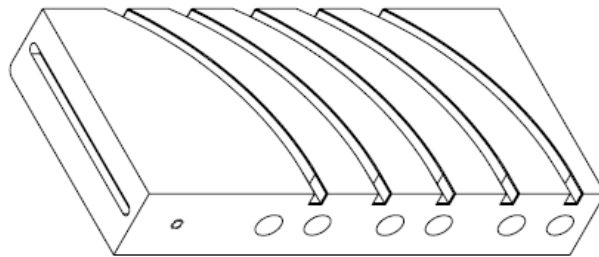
Molde de curvado y calentamiento. Fuente: Base de datos de Boston Scientific.
